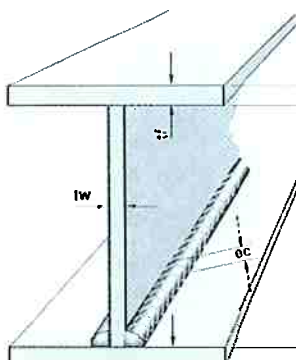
Detalhe do cordão de solda nos perfis soldados⁽²⁶⁾
